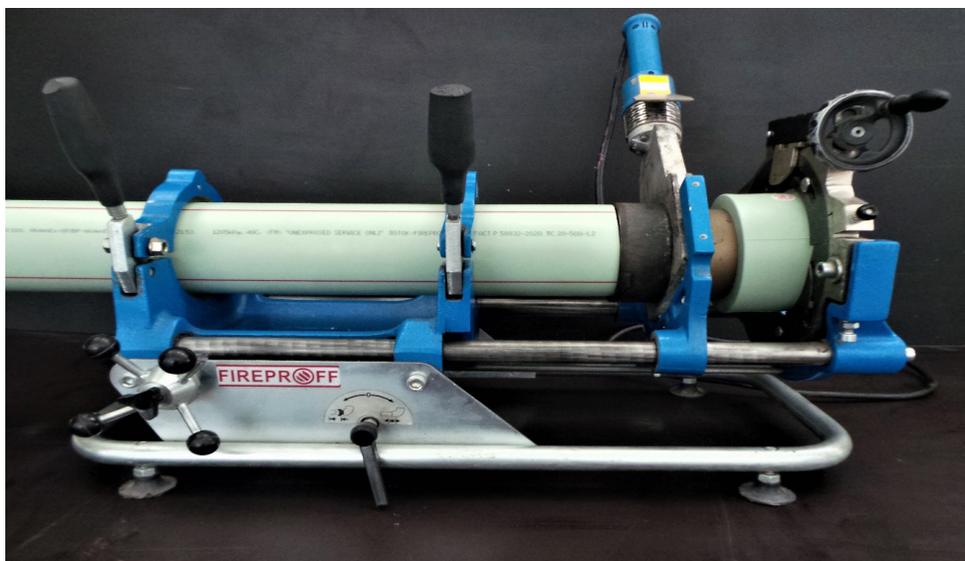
Фиксация, подготовка к нагреву и нагрев элементов трубы в сварочном аппарате.
